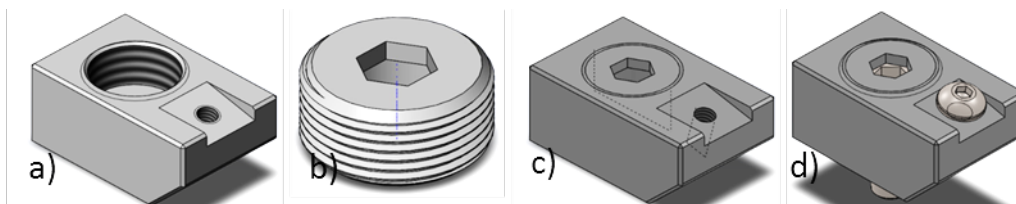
Sujetador a) elemento para posicionar, b) elemento opresor, c) unión de elementos, d) ensamble.
